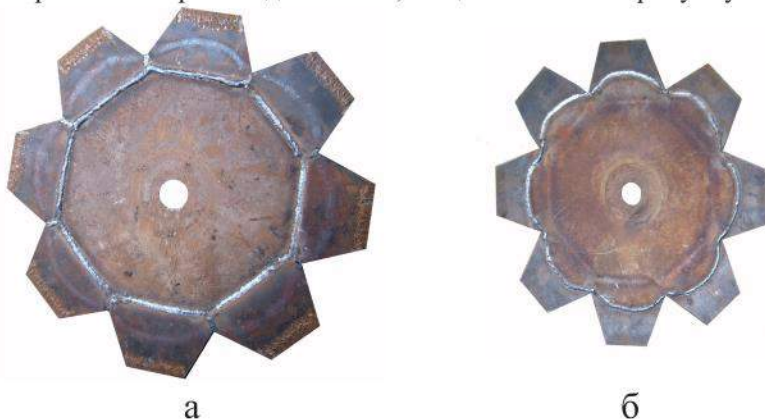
Відновлений диск приварюванням зубів з робочої сторони (а) та неробочої сторони (б)
